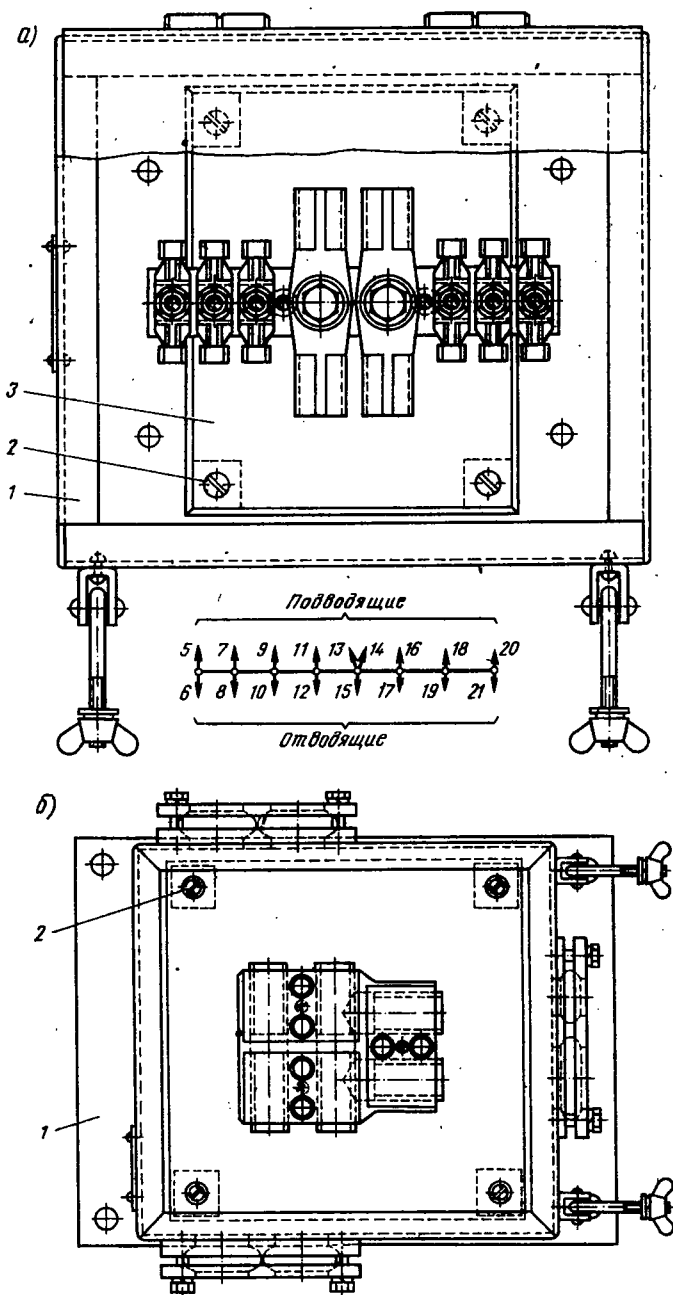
Общий вид соединительной коробки СК-25Ж (а)
